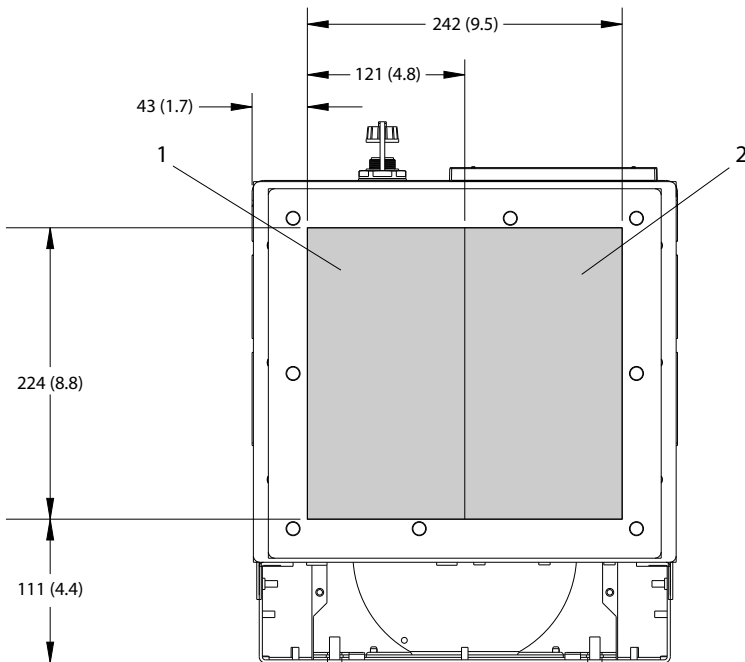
Dimensi Akses Heat Sink untuk D5h
